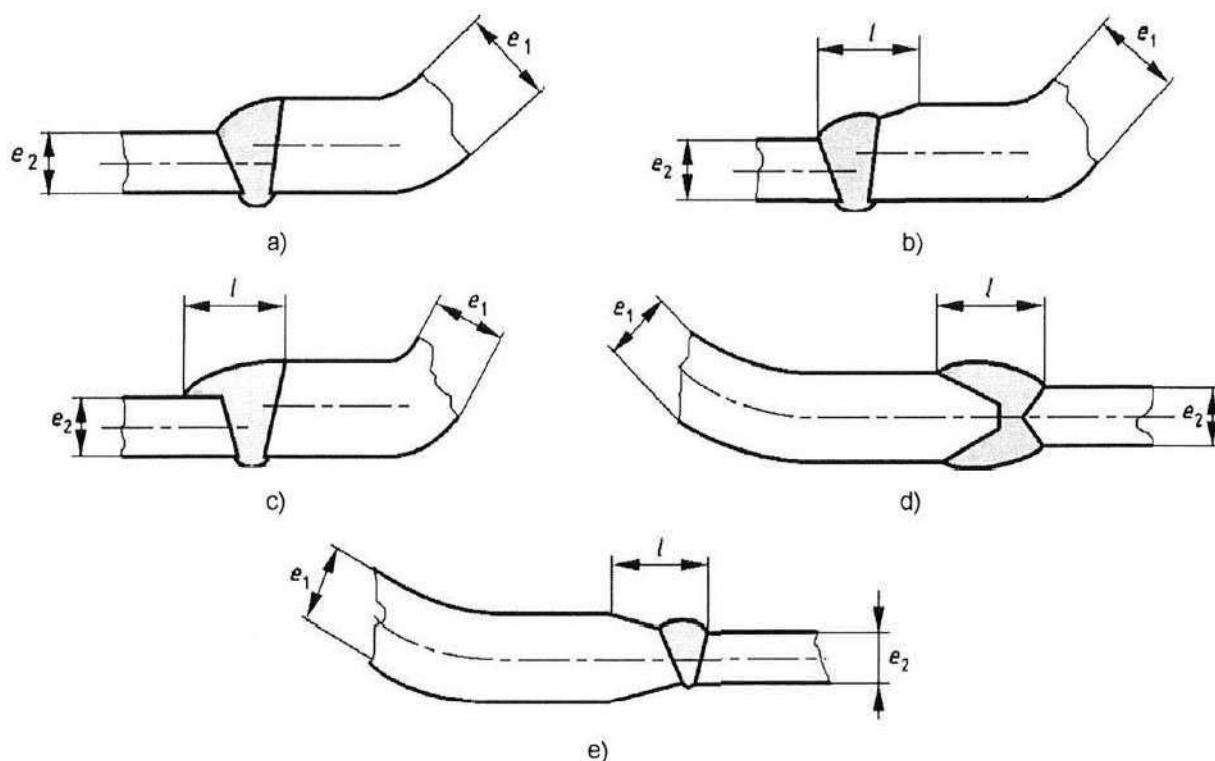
Примеры типовых стыковых швов, соединяющих корпус с торцом
